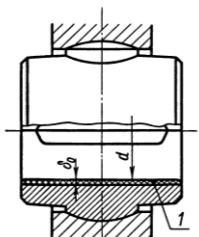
Самоустанавливающийся подшипник: 1 – баббитовая заливка
